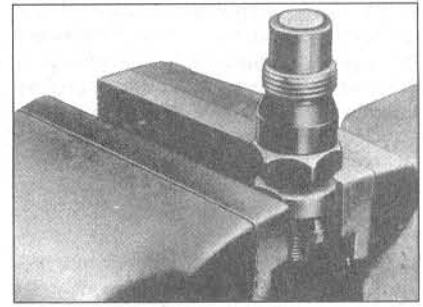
Способ закрепления форсунки перед разборкой (Глава 37)
